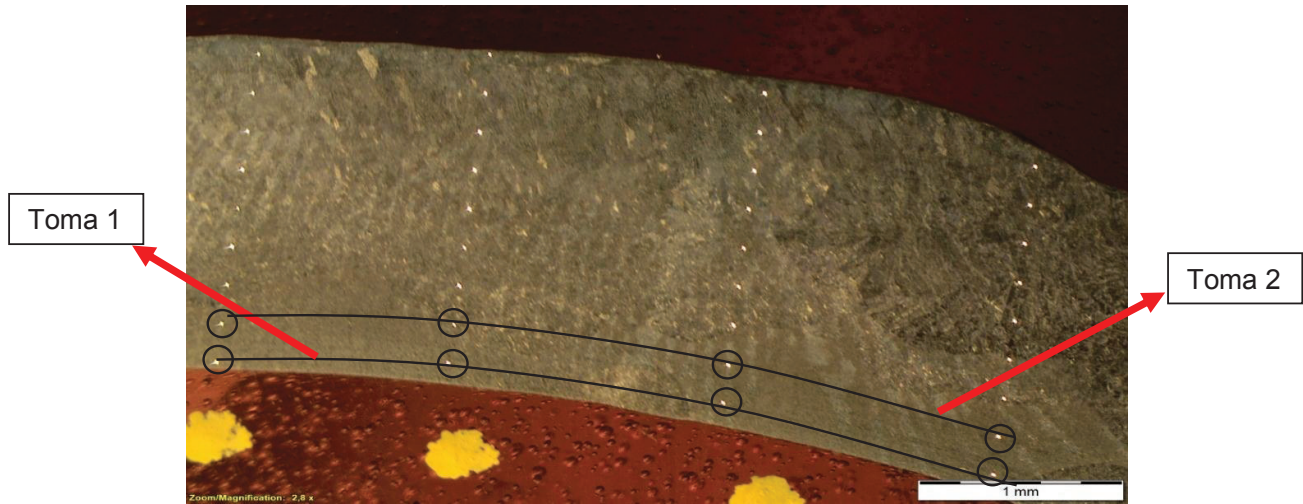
Posiciones y tomas de dureza del cordón de soldadura.
